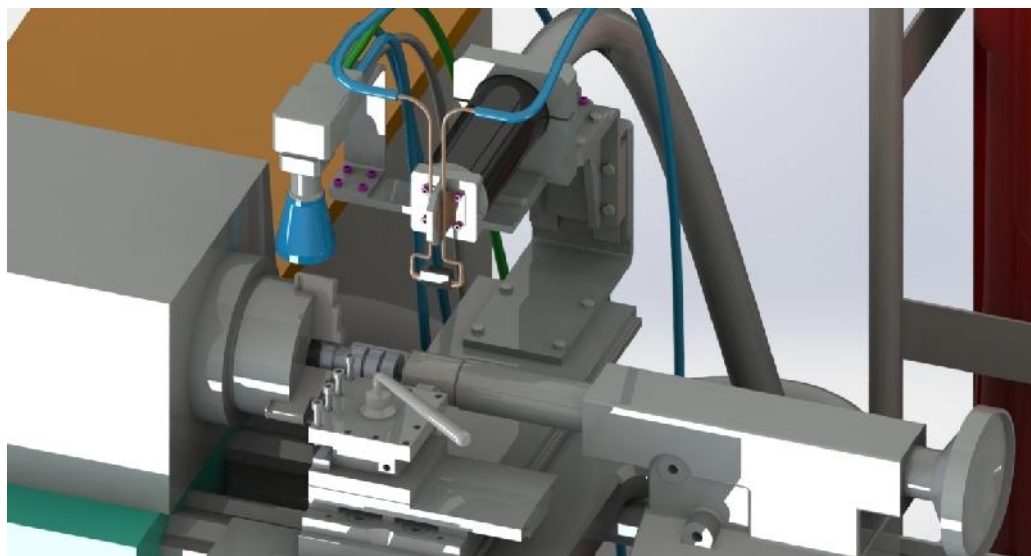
Рабочая зона гибридного станочного комплекса на базе токарного станка
